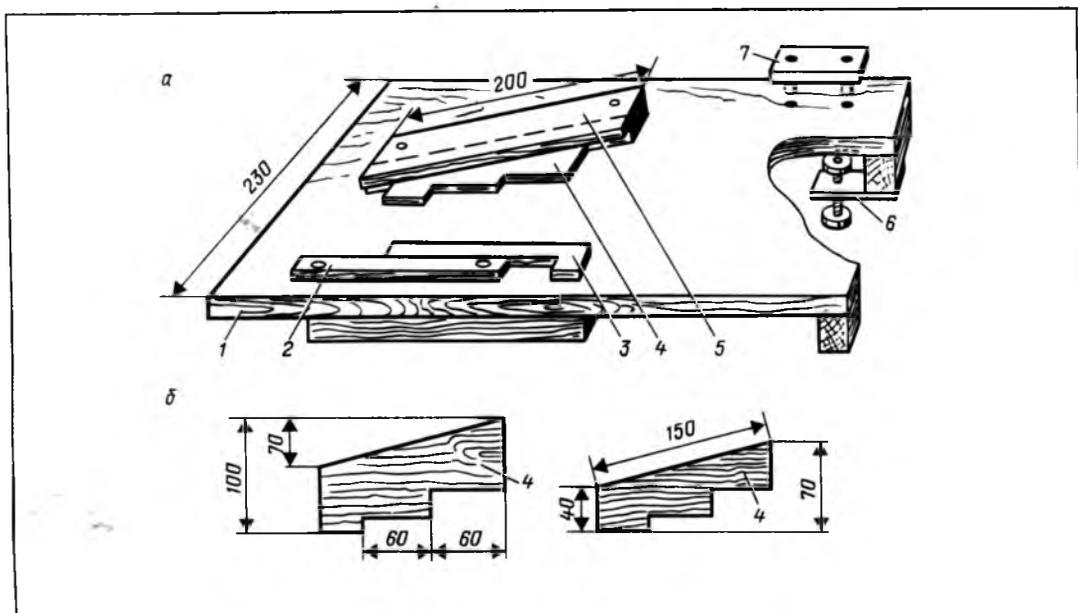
Съемная крышка столярного верстака: а — конструкция крышки (1 — основание; 2 — боковая рейка; 3 — вкладыш; 4 — упор для строгания; 5 — направляющая; 6 — струбцина для крепления верстака к крышке стола; 7 — упор для пиления); б — сменные упоры для строгания
